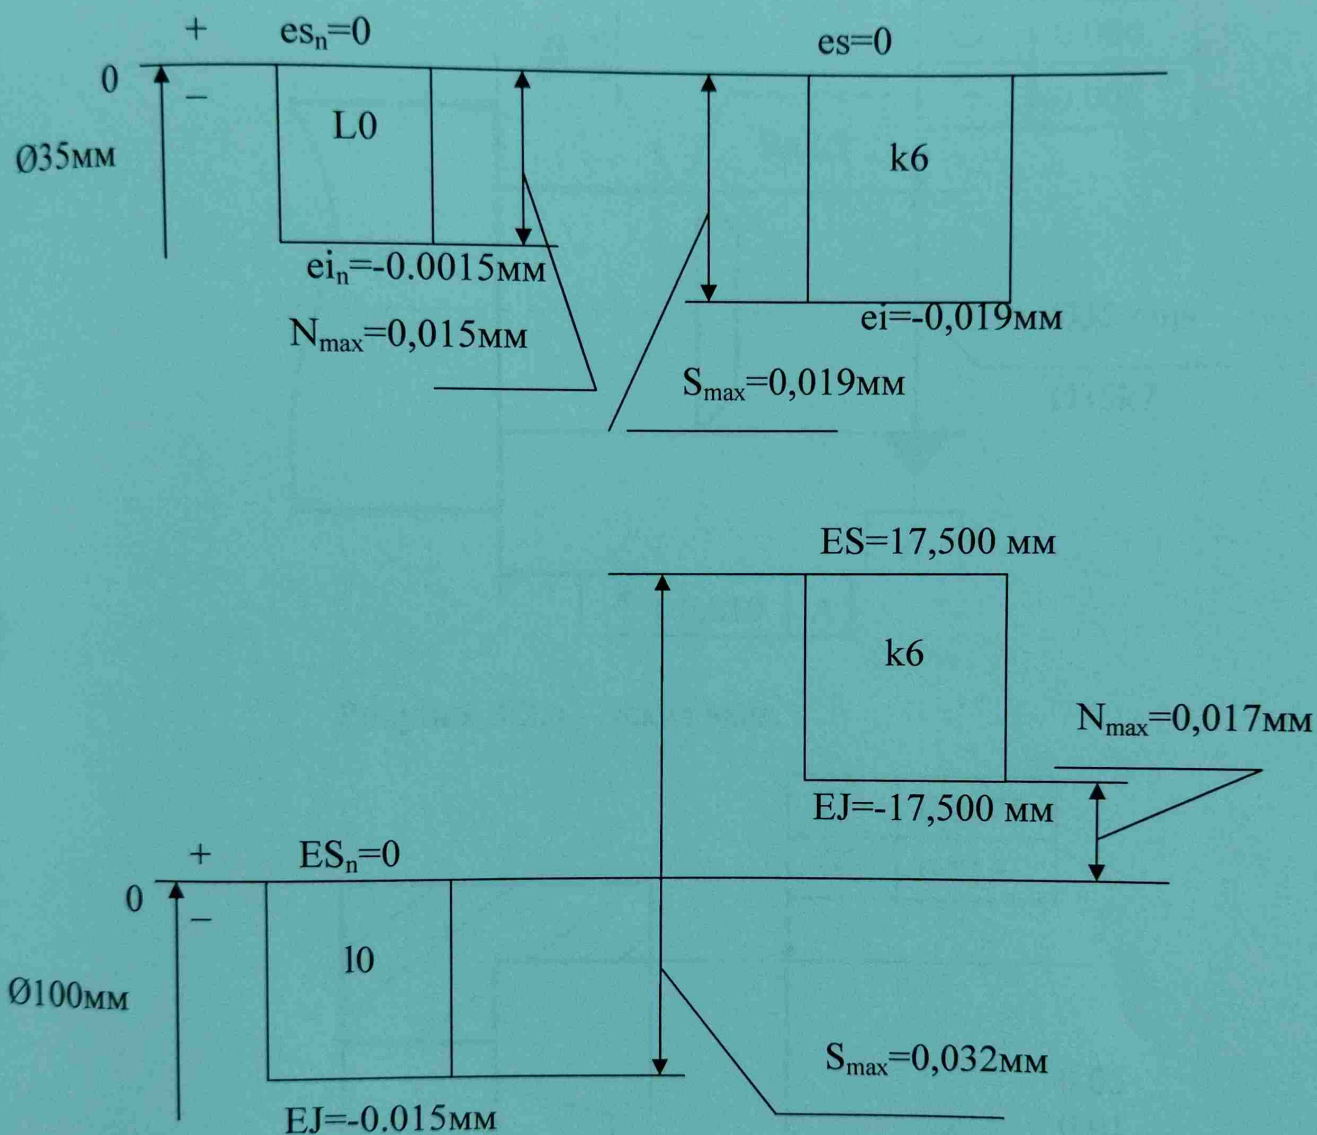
Схема расположения полей допусков для деталей подшипникового узла.
